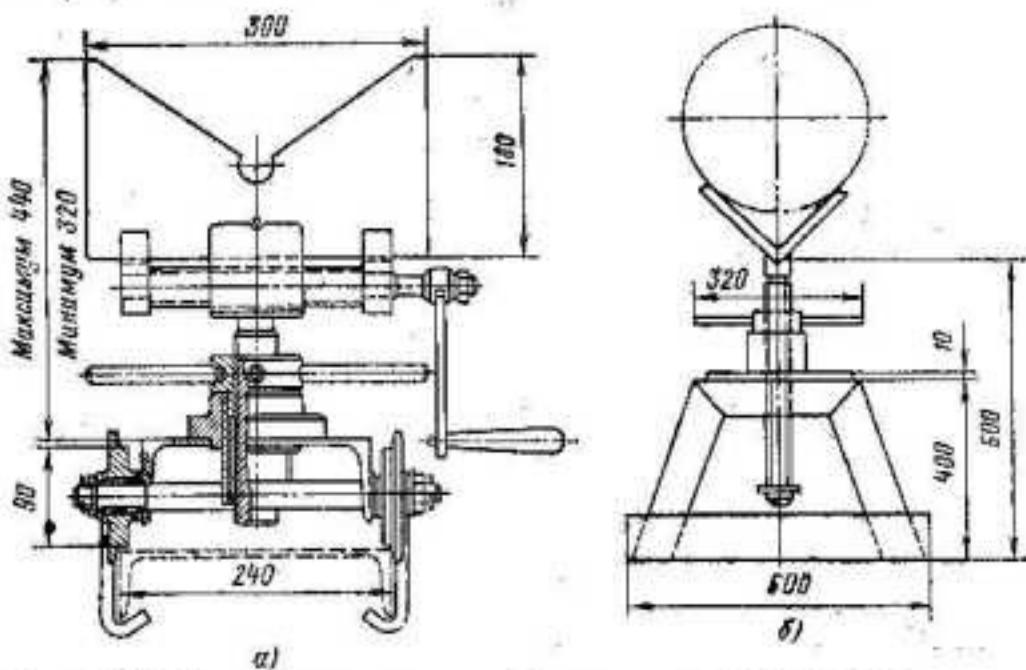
Центровочные приспособления для сборки блоков.
